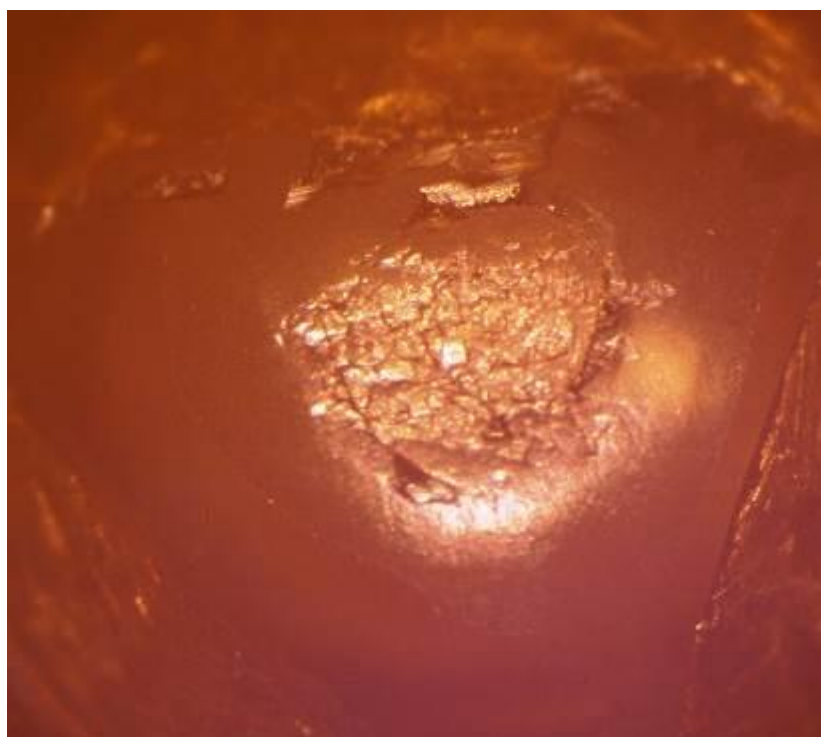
Очаг износа выглаживающего инструмента из твердого сплава ВК-ОМ
